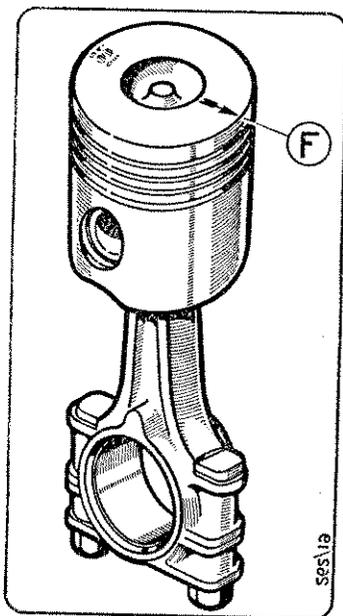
RIFERIMENTO MONTAGGIO PISTONE
